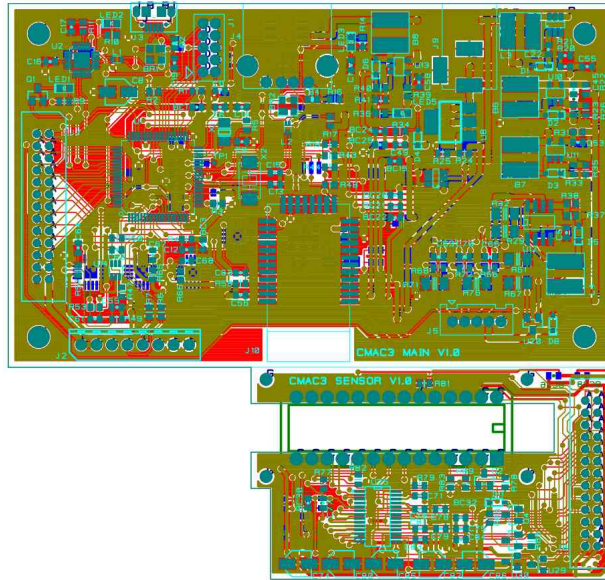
PCB Total layer (4 layer) Top에 대한 Drawing 이미지
